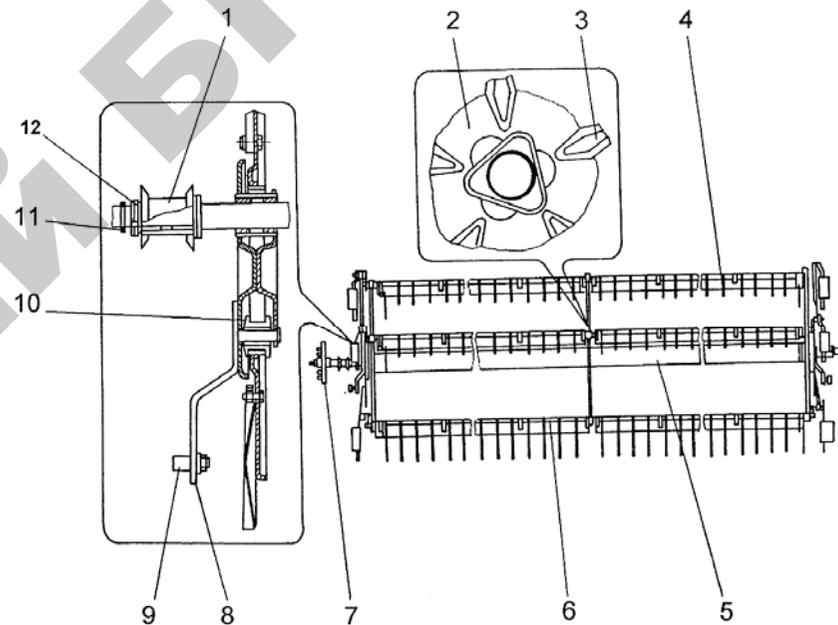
Мотовило: 1 — подшипник; 2 — диск; 3 — луч; 4 — зуб пружинный; 5 — труба центральная; 6 — граблина; 7 — звездочка с предохранительной муфтой; 8 — поводок; 9 — ролик; 10 — механизм эксцентриковый; 11 — кольцо; 12 — шайбы регулировочные
